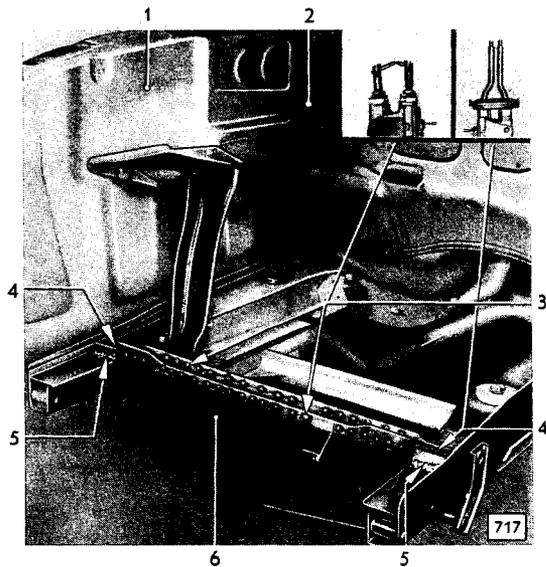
Vorderrahmenquerträger an Längsträger und Obergurt punktschweißt
